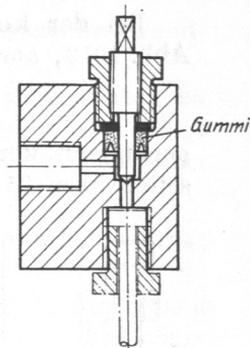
Spindelabdichtung mittels gespaltenen Gummirings.
